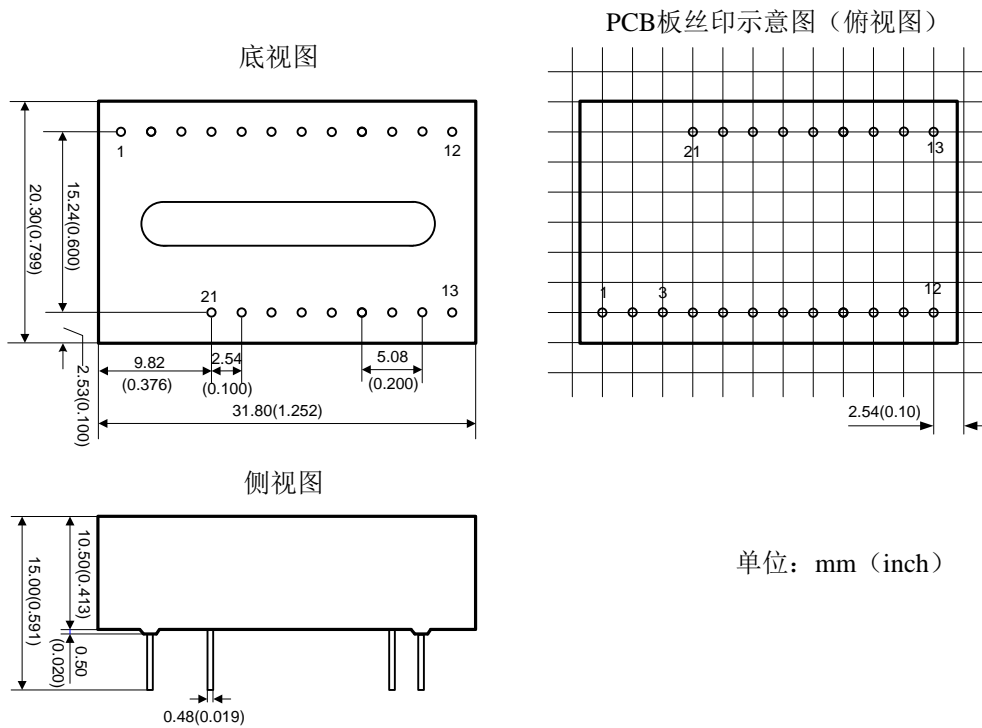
RSM232P 机械尺寸及 PCB 丝印示意图
